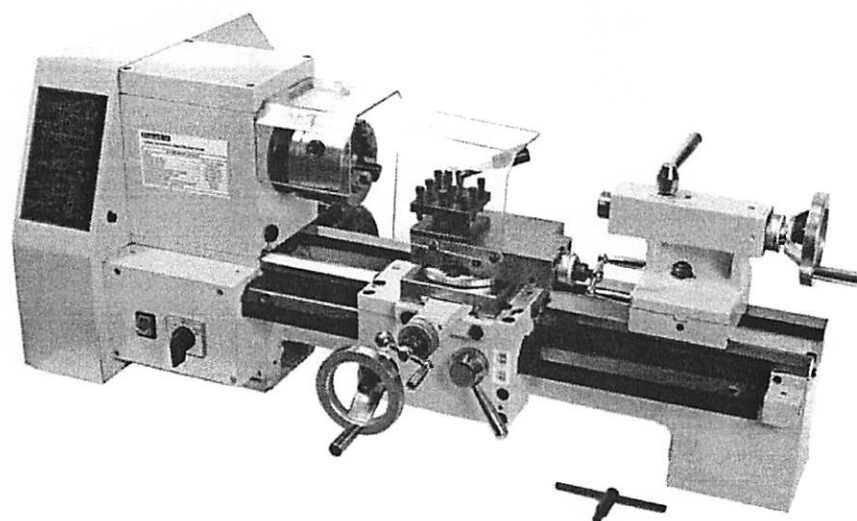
Torno Elétrico Universal Ferrari BV-20
